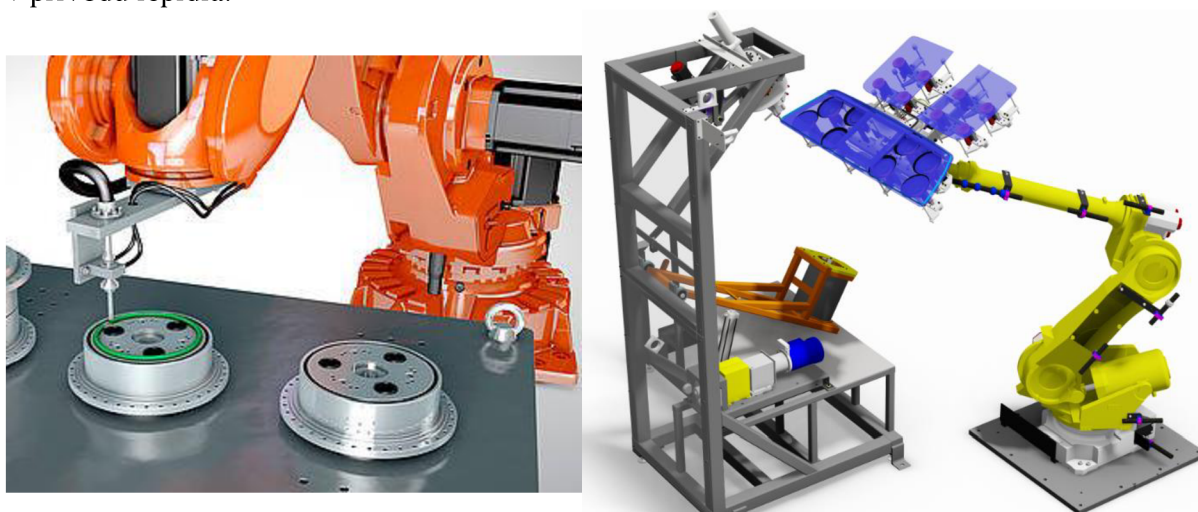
a) Kartézský robot [43], b) Šestiosý robot [44]
